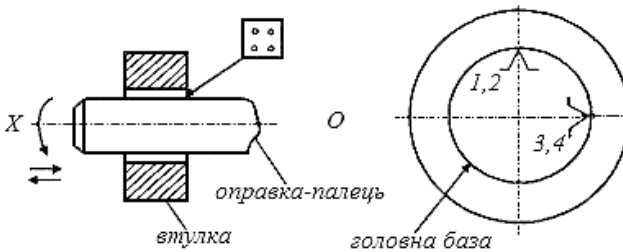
Схема базування по внутрішнім циліндричним поверхням [2]
